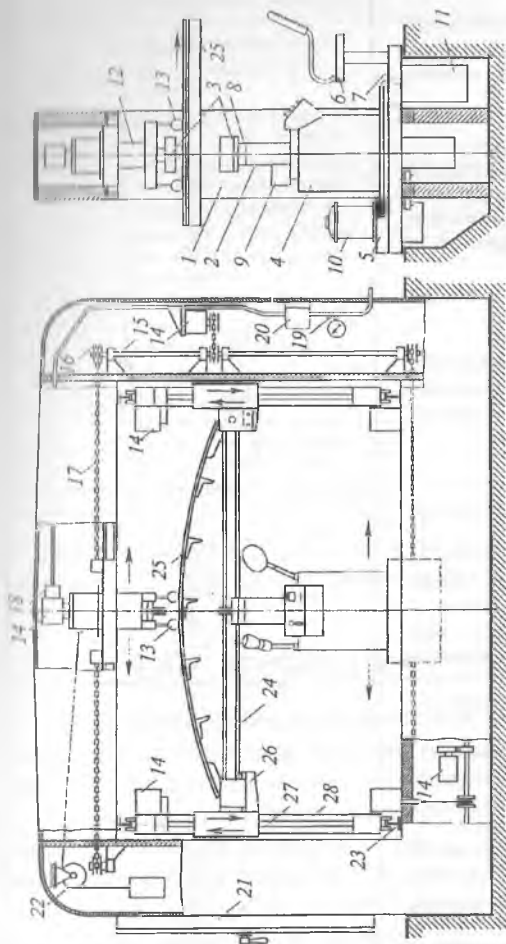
Конструкция пресса КП-602: 1 — станина;
